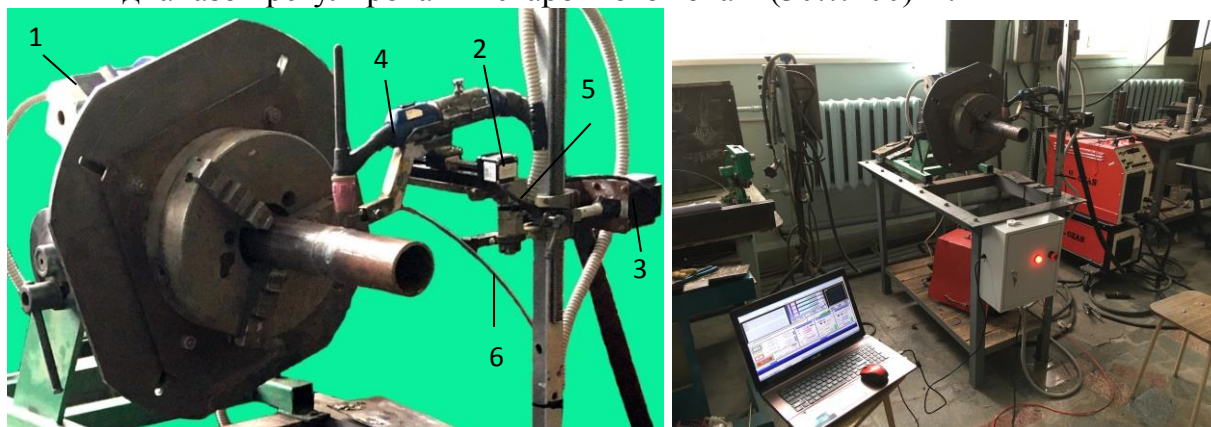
Внешний вид установки автоматической сварки тел вращения
